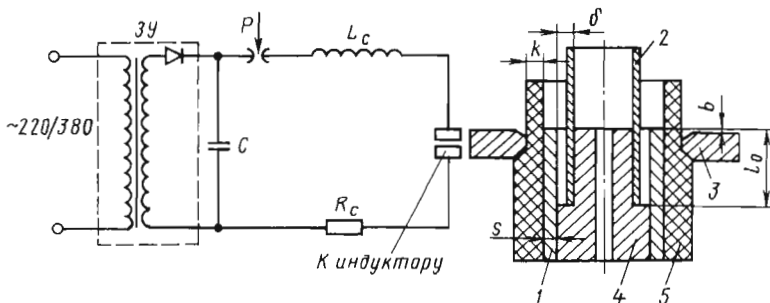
Принципиальная схема магнитно-импульсной сварочной установки:
